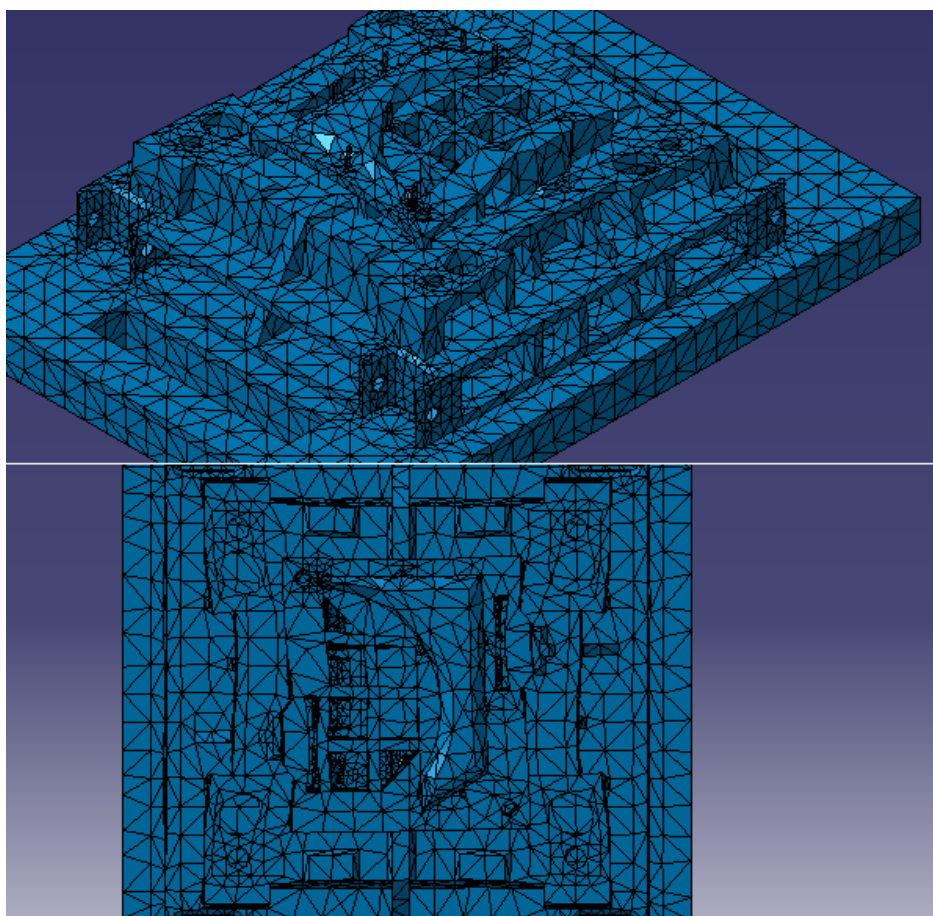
Deformada para espessura de 100mm (Fonte – Construção própria)
